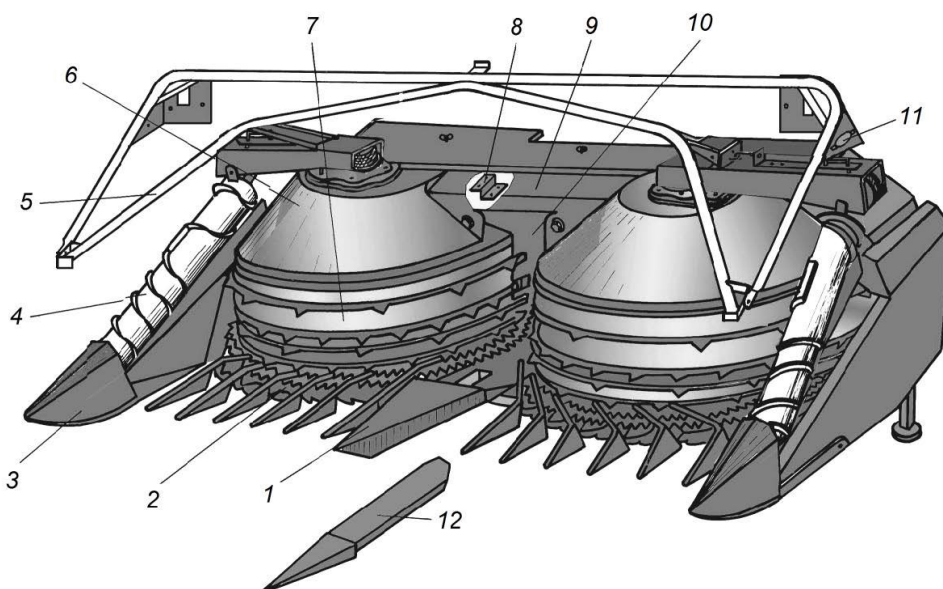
Жатка для грубостебельных культур: 1 – средний делитель; 2 – режущий ротор; 3 – башмак бокового делителя; 4 – боковой делитель; 5 – заламывающий брус; 6 – кожух; 7 – барабан; 8 – кронштейн; 9 – крышка; 10 – кожух скребков; 11 – световозвращатель; 12 – сменный средний делитель
